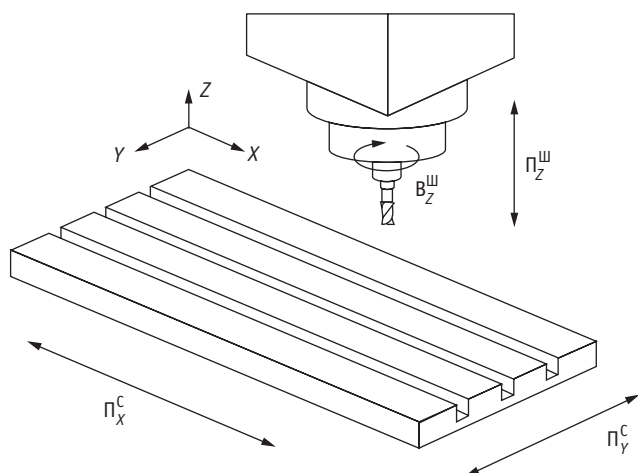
Формообразующие движения рабочих органов станка Mazak Smart 430A
